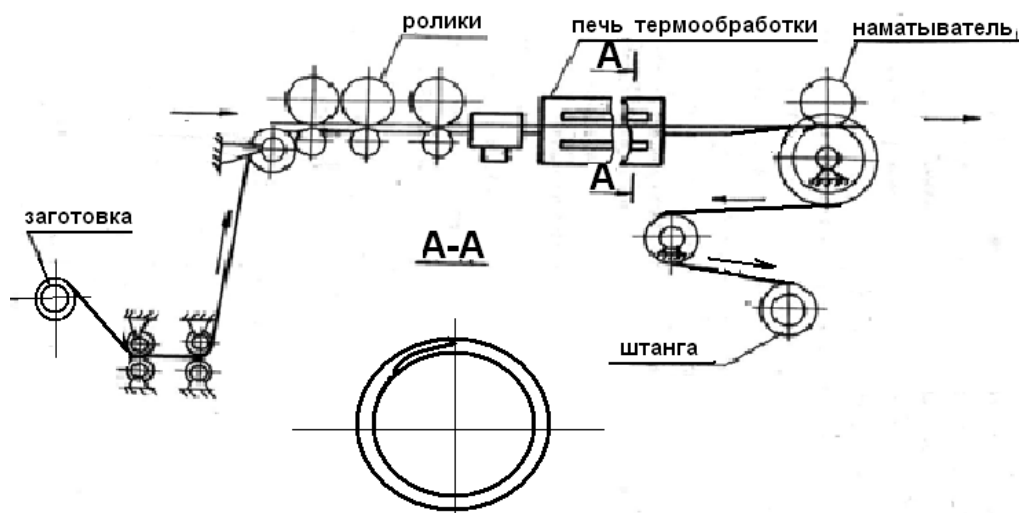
Схема установки для изготовления трубчатых заготовок штанг
